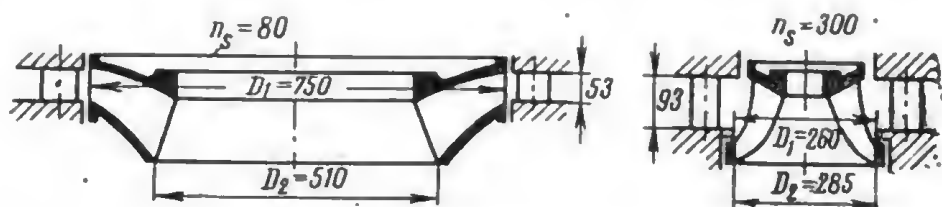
Габариты приведенных рабочих колес различной быстроходности.
